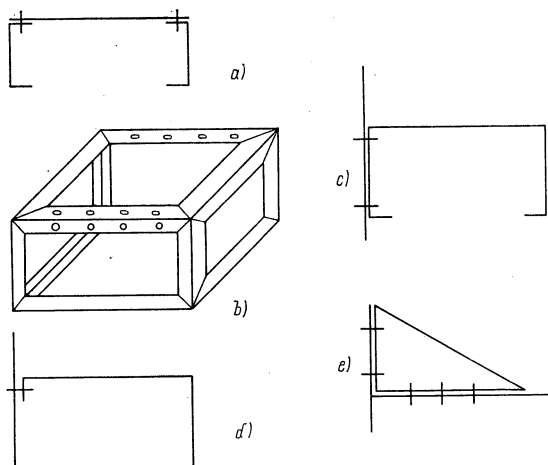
Chassisformen II; a — bestehend aus Aufbauplatte und 2 U-Schienen, b — Rahmen aus Winkelmaterial für Versuchschassis in Streifenbauweise, c — und d — Chassis mit Frontplatte, e — Front- und Chassisplatte werden durch Dreieckbleche verbunden
